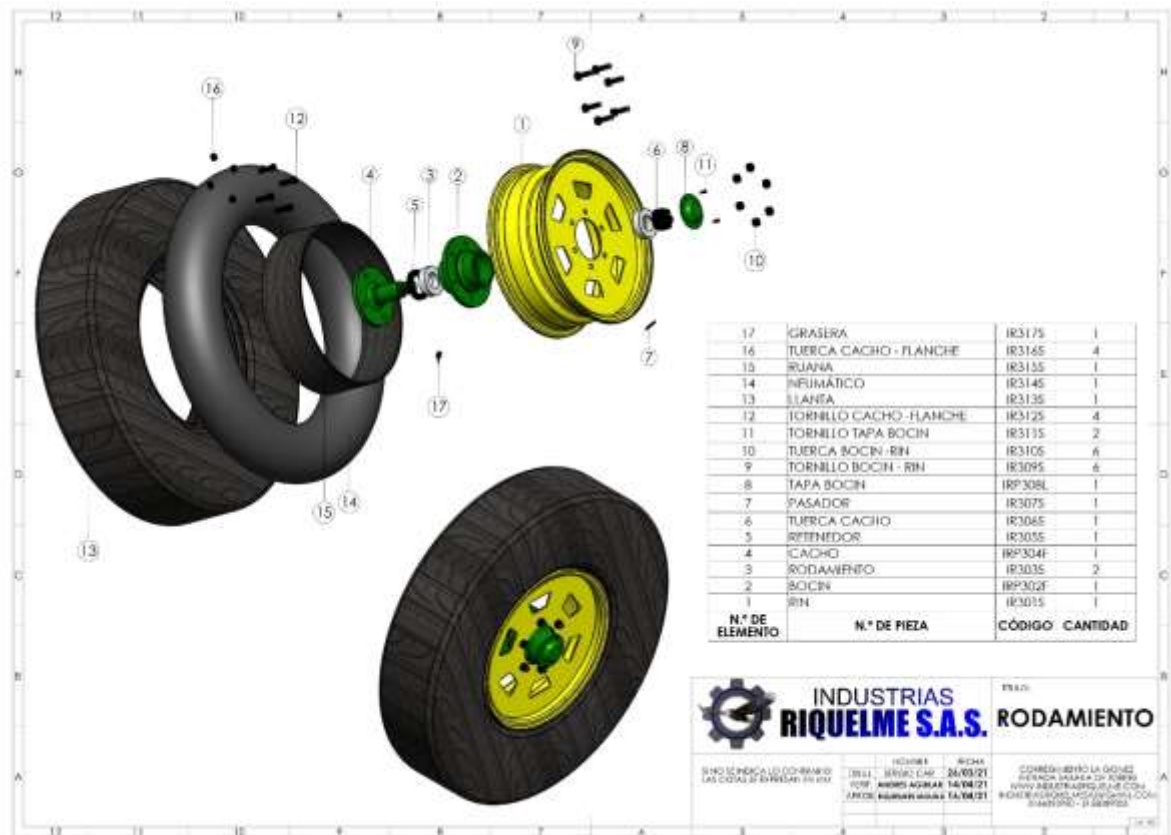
Plano mecánico ejes vista isométrica - explosionada
